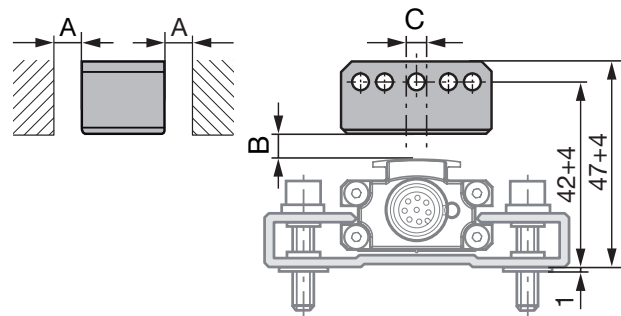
Dimensions et distances pour le capteur de position BTL6-A-3801-2
